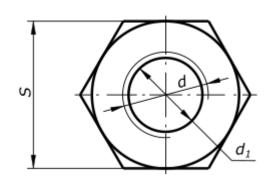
Чертеж гайки с привязкой габаритов
